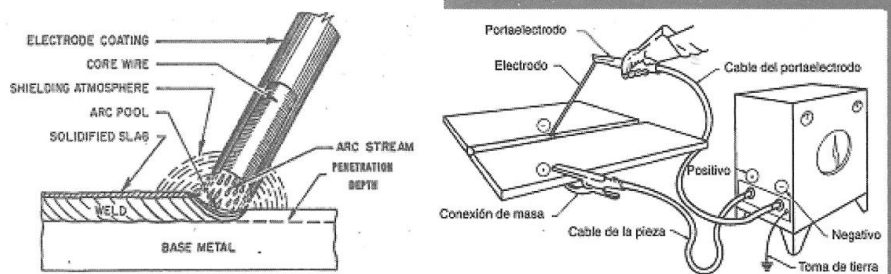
Proceso de soldadura por arco con electrodo revestido.
